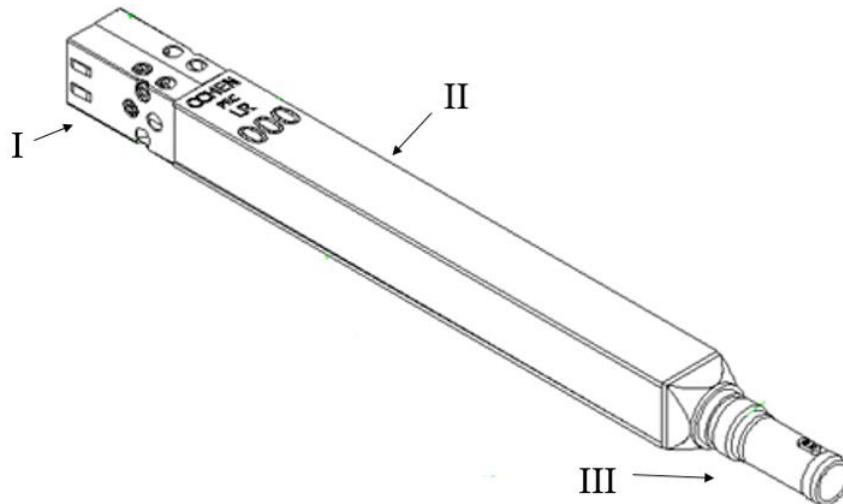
Vista isométrica del Elemento Combustible MTR 3,4 [ $gU/cm^3$ ]. Fuente imagen: CCHEN [1].
